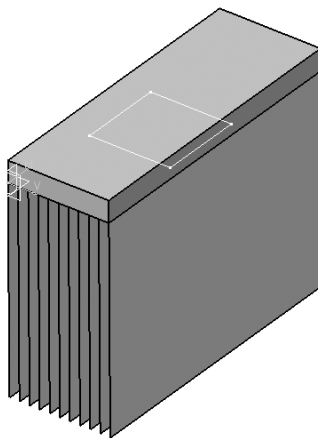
Modelo 3D em CAD do dissipador patente 5201866.
